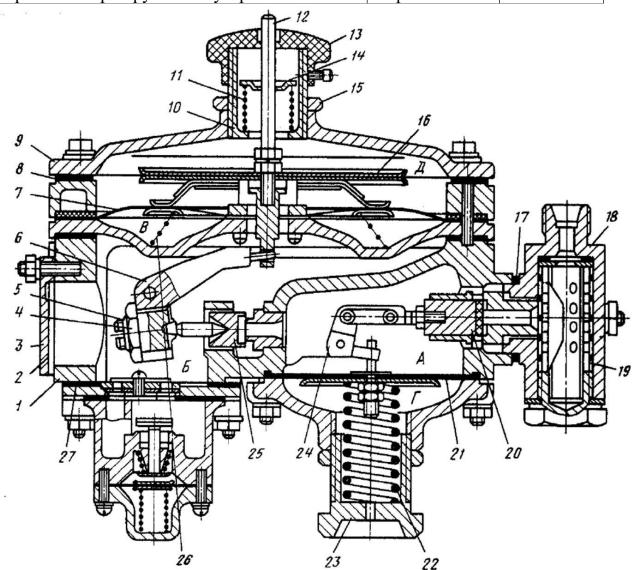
Газовый редуктор низкого давления: А - полость первой ступени; Б - полость второй ступени; В - полость разгрузочного устройства; ГиД- полости атмосферного давления; 1 - корпус газового редуктора; 2 - прокладка; 3 – крышка; 4 - контргайка регулировочного винта: 5 - регулировочный винт клапана низкого давления: 6 - рычаг диафрагмы низкого давления; 7 - разгрузочная диафрагма; 8 - прокладка разгрузочной диафрагмы; 9 - крышка корпуса верхняя; 10 - седло пружины диафрагмы низкого давления; 11 - пружина диафрагмы низкого давления: 12 - шток диафрагмы низкого давления; 13 - регулировочный ниппель пружины; 14 - шайба упорная пружины; 15-контргайка седла; 16 - диафрагма низкого давления; 17 - прокладка корпуса фильтра; 18 - фильтр газового редуктора; 19 - сетка фильтра; 20 - клапан высокого давления; 21 - диафрагма высокого давления; 22 - пружина диафрагмы высокого давления;
